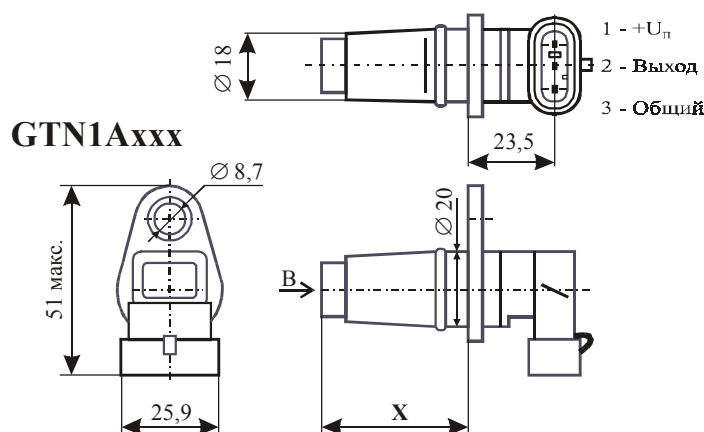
Внешний вид и габаритные размеры датчиков серии GTN1A
